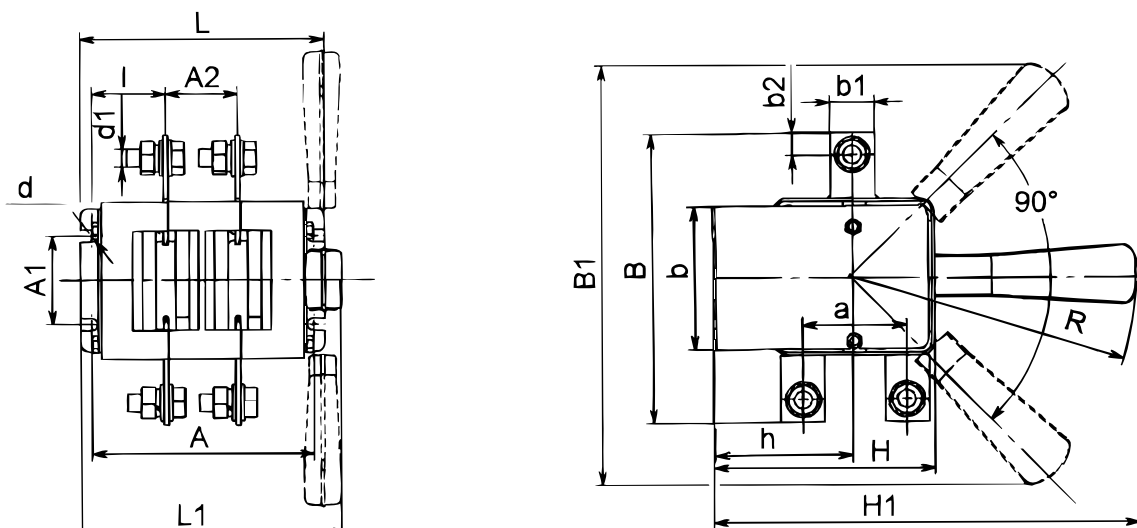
Выключатель-разъединитель на два направления двухполюсный с боковой рукояткой
